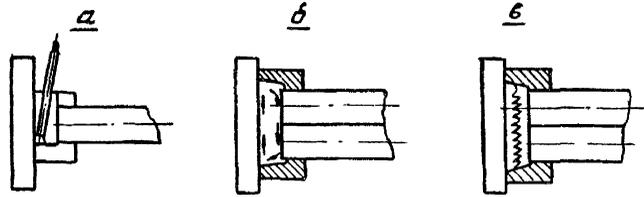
Техника многослойной сварки в медной форме тавровых соединений сваренных стержней с пластиной.
